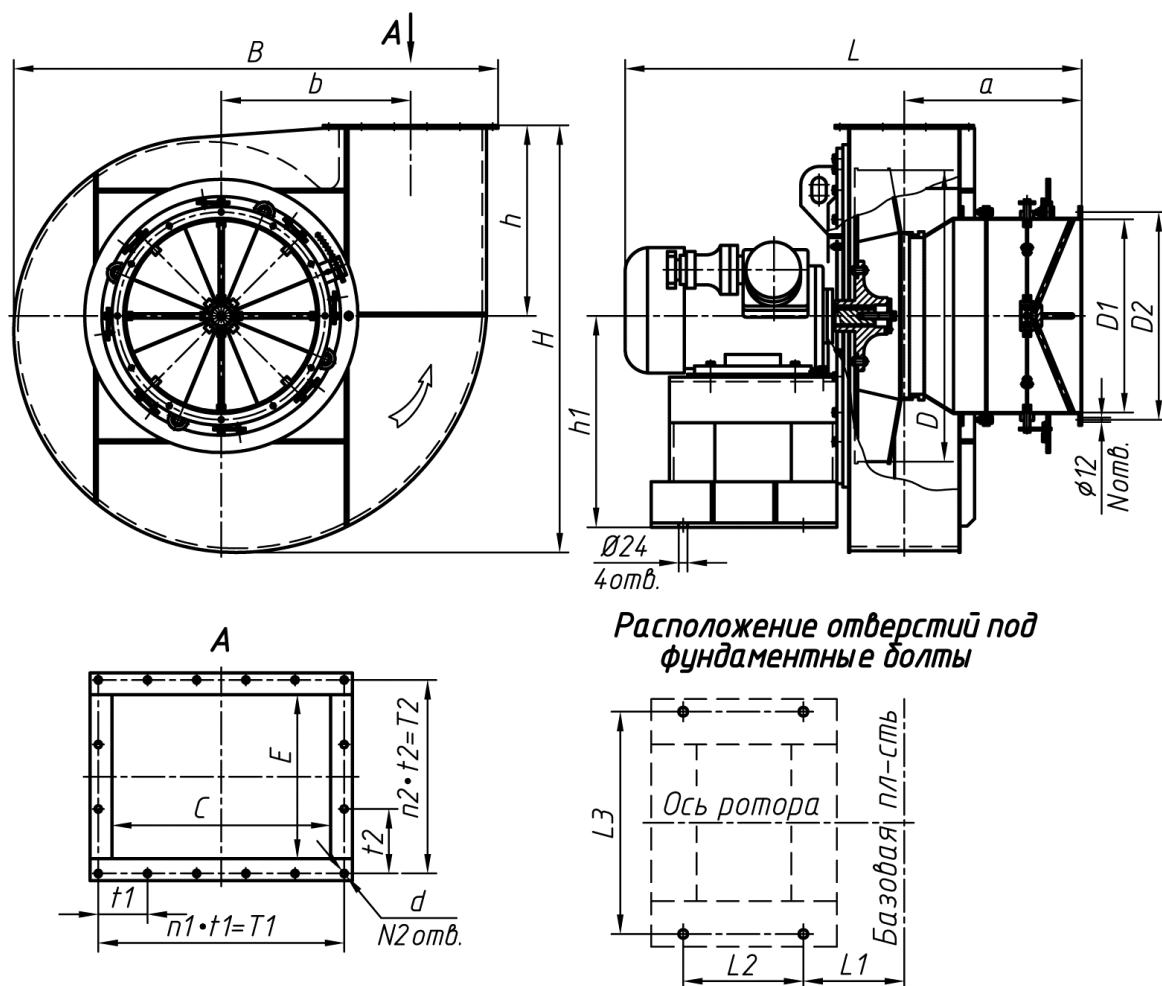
Габаритные и присоединительные размеры центробежных тягодутьевых машин исполнения 1 ВД, Д №6,3÷12.
